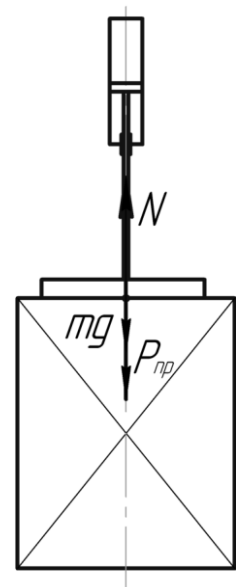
Розрахункова схема для підбору пневмо-циліндра пристрою прижимання пакету
